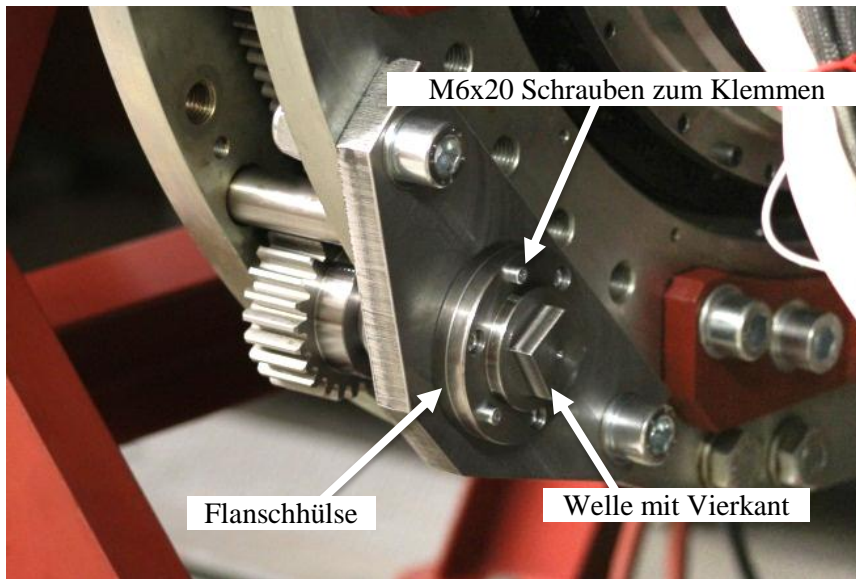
Zahnradbefestigung mit Klemmwelle
